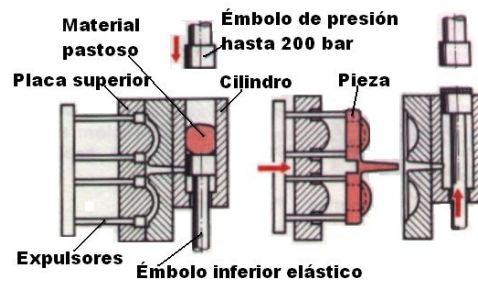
Fundición a presión. Método de la cámara caliente
